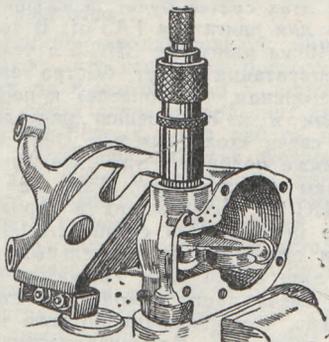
Установка игл подшипника во втулку цилиндра подвески при помощи приспособления.
